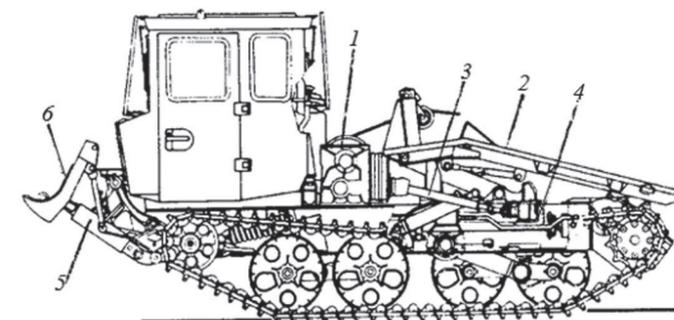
Технологическое оборудование чokerного трелевочного трактора: 1 – реверсивная лебедка; 2 – шит; 3 – вал привода лебедки; 4 – редуктор привода лебедки; 5 – гидроцилиндр привода толкателя; 6 – толкатель
